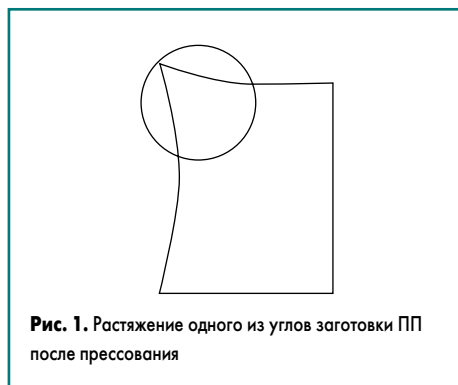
Растяжение одного из углов заготовки ПП после прессования
